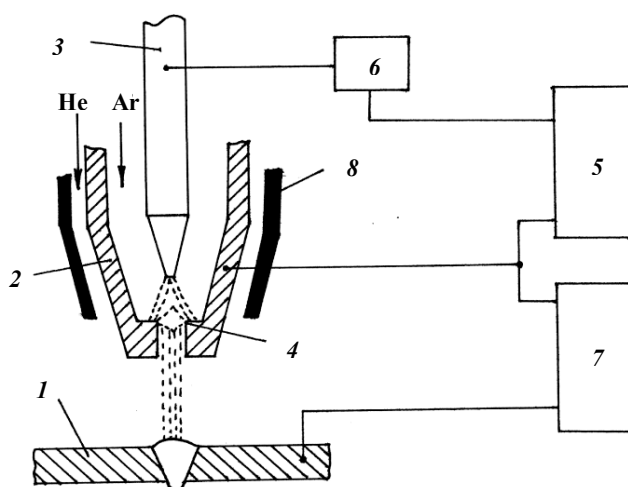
Схема процесса плазменной сварки протяженных швов полотнищ из алюминиевых сплавов:
